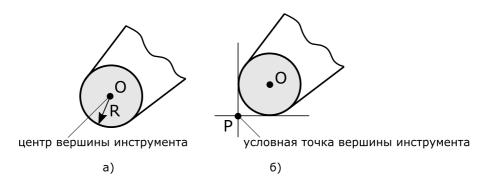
Положение центра вершины инструмента (а) и его вершины (б). R – значение радиуса вершины инструмента
